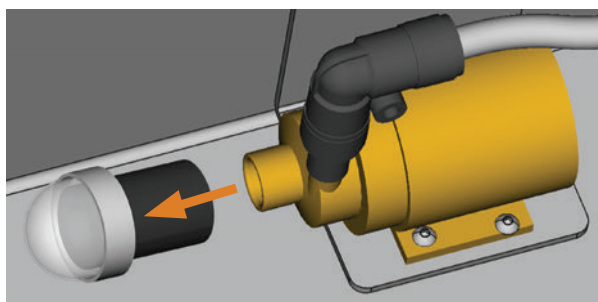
RETIRAR EL FILTRO DE LA BOMBA
